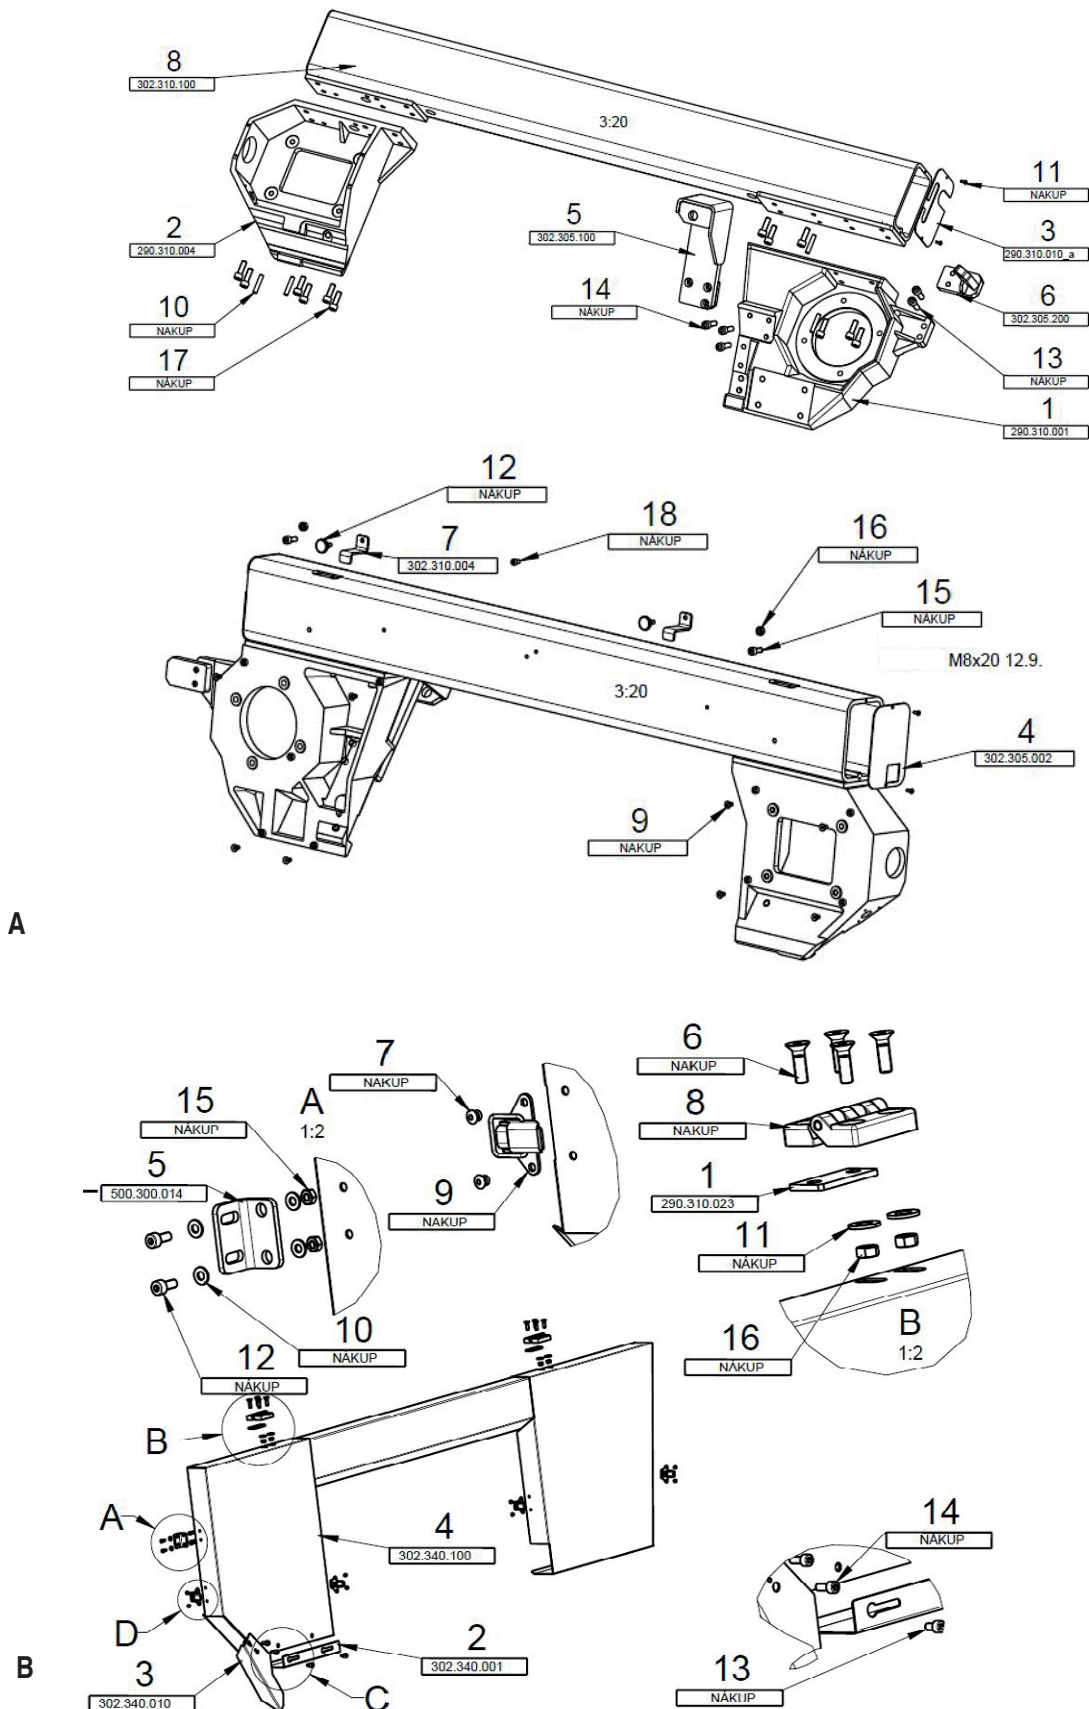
Dessin des pièces détachées 5 A : Châssis du bras de la scie, B : Carter de protection
